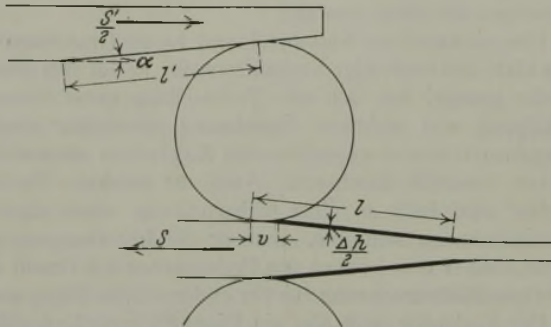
Werkstoffverdrängung beim Krause-Walzverfahren.
